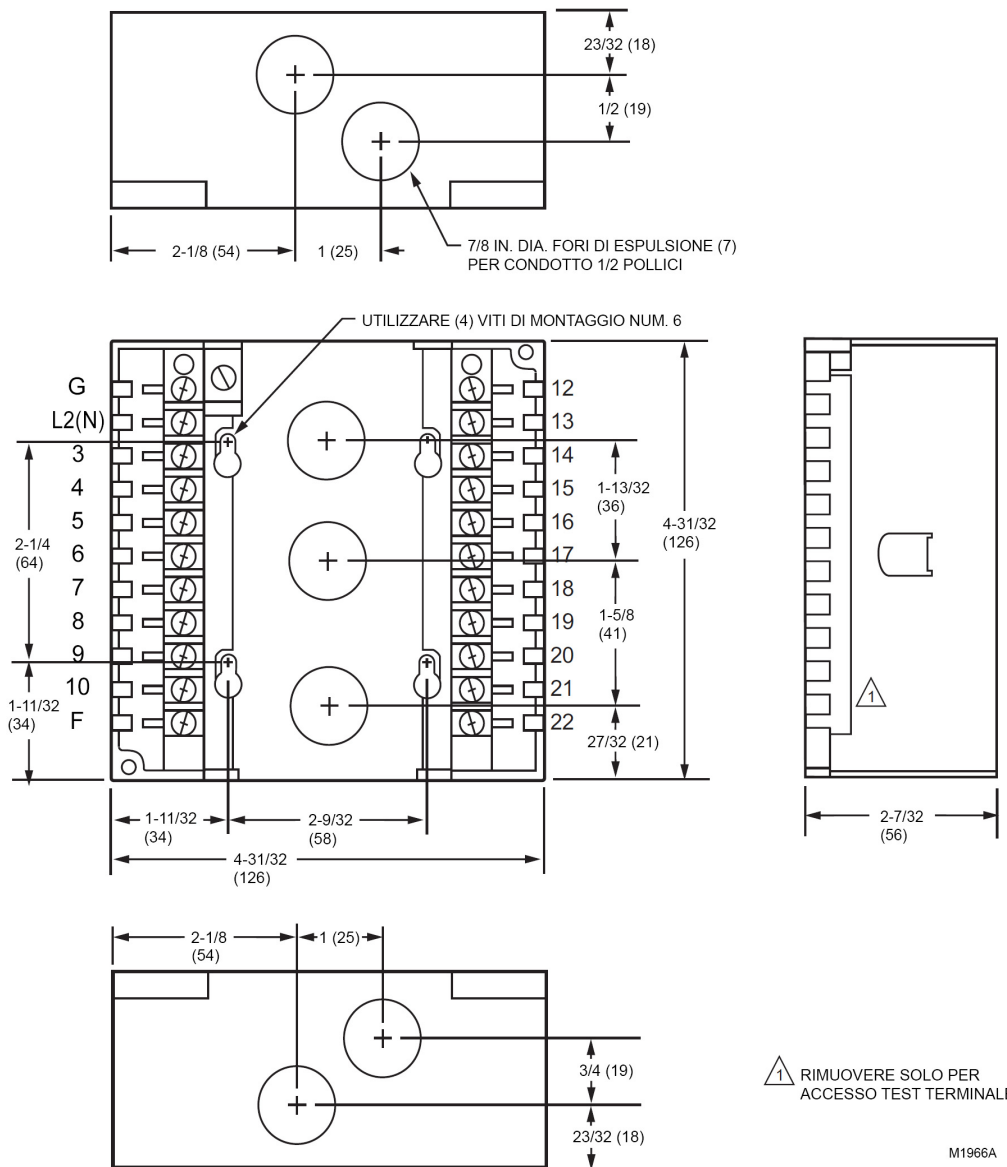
Vista superiore e frontale della sottobase di cablaggio Q7800B1003 (4 lati) con dimensioni in pollici (mm).
